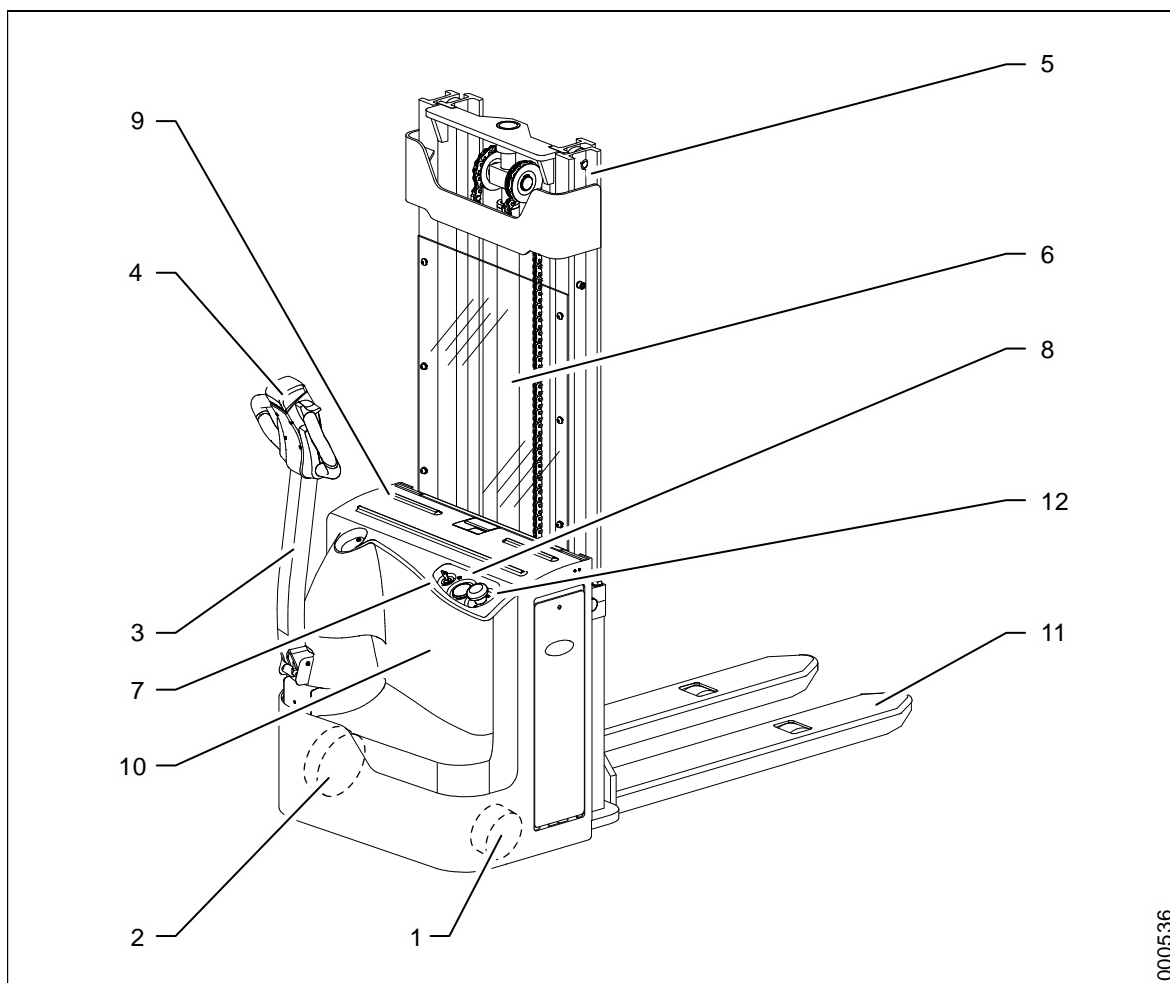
Vue d'ensemble du chariot WSX12/ WSX14
